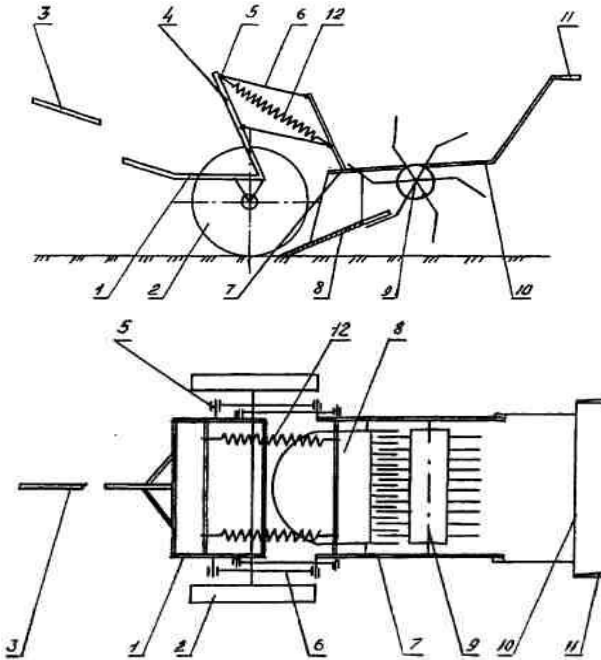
Схема кінного картоплекопача роторного типу: 1 – рама; 2 – опорно-приводне колесо; 3 – дишло; 4 – консоль; 5 – шарнір; 6 – повідець; 7 – рухома рама; 8 – леміш; 9 – ротор; 10 – оперечина; 11 – ручка; 12 – зрівноважувальний механізм
